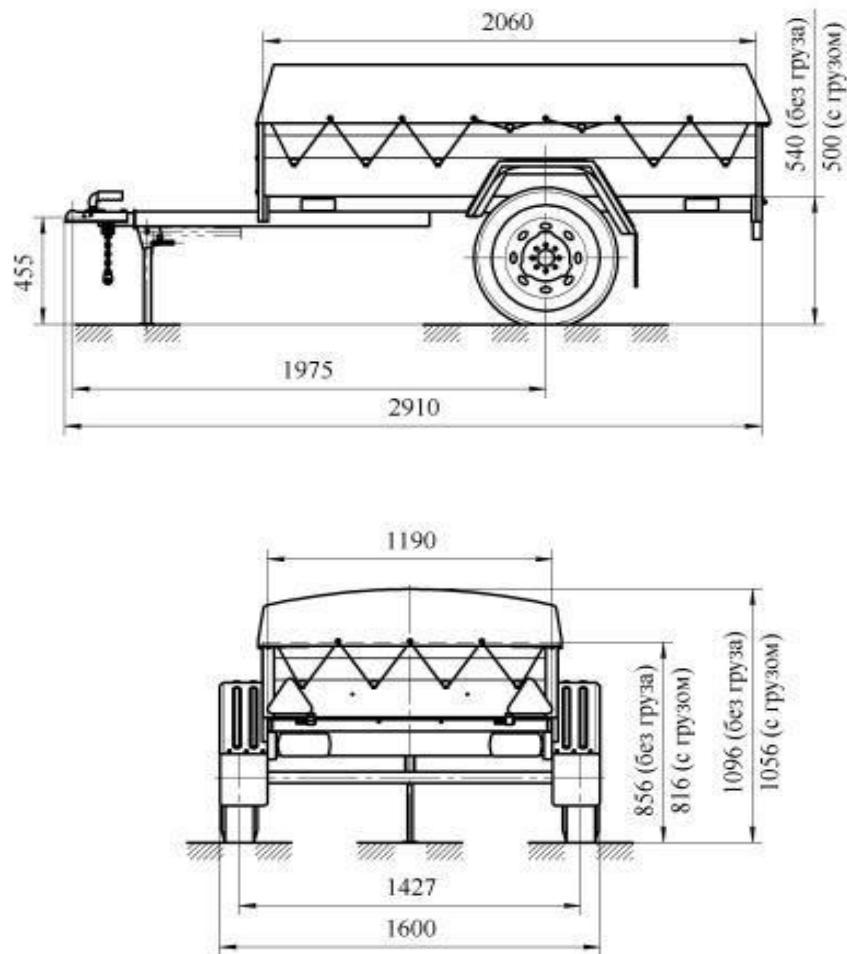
Загальний вид прицепа «ПГМФ -8232»
